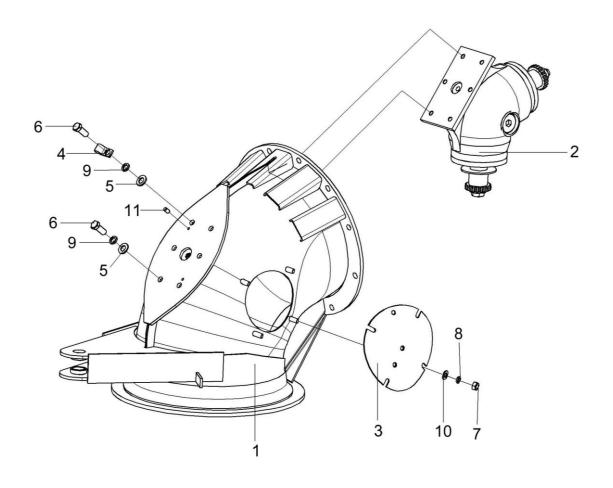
Отвод с редуктором КЗК-12-0206090А
